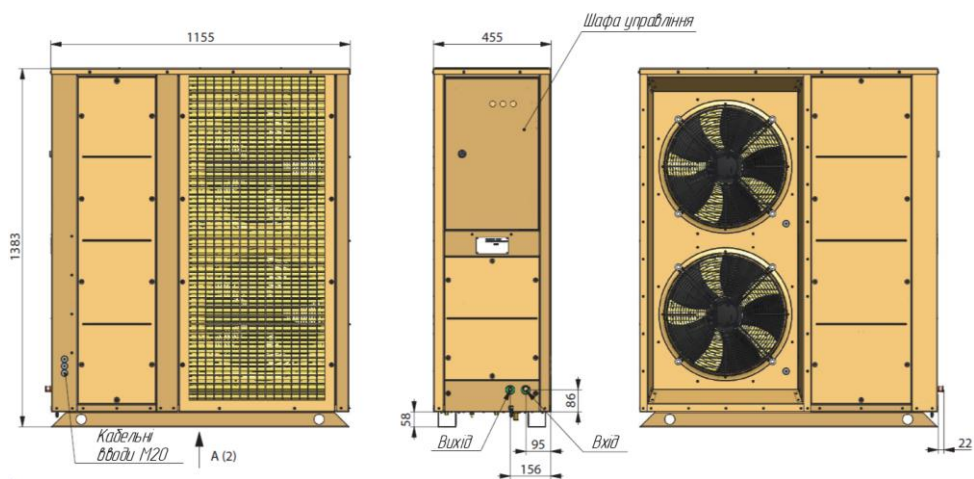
Загальний вид агрегату типу МАКК-110-51, МАКК-110-81
